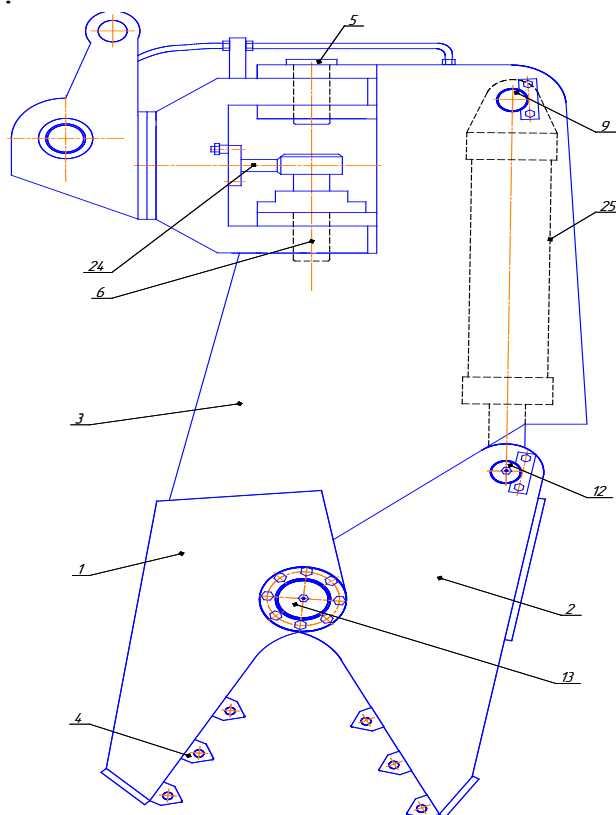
Рабочее оборудование для захвата и разрушения строительных конструкций
